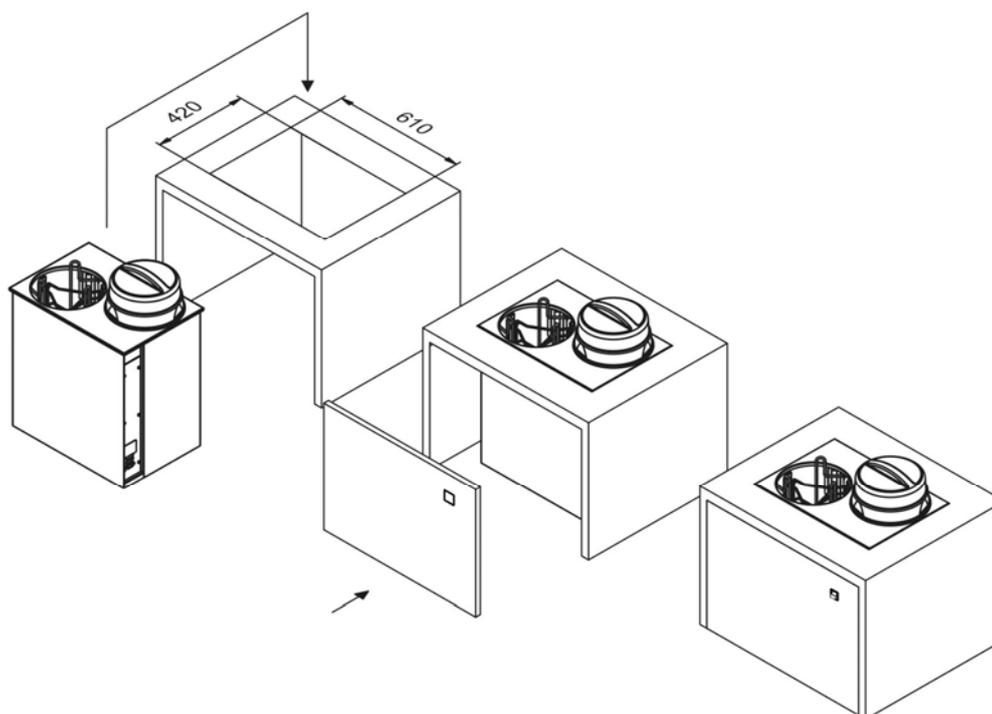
Instrucciones de montaje EBRH-2/V19-26
